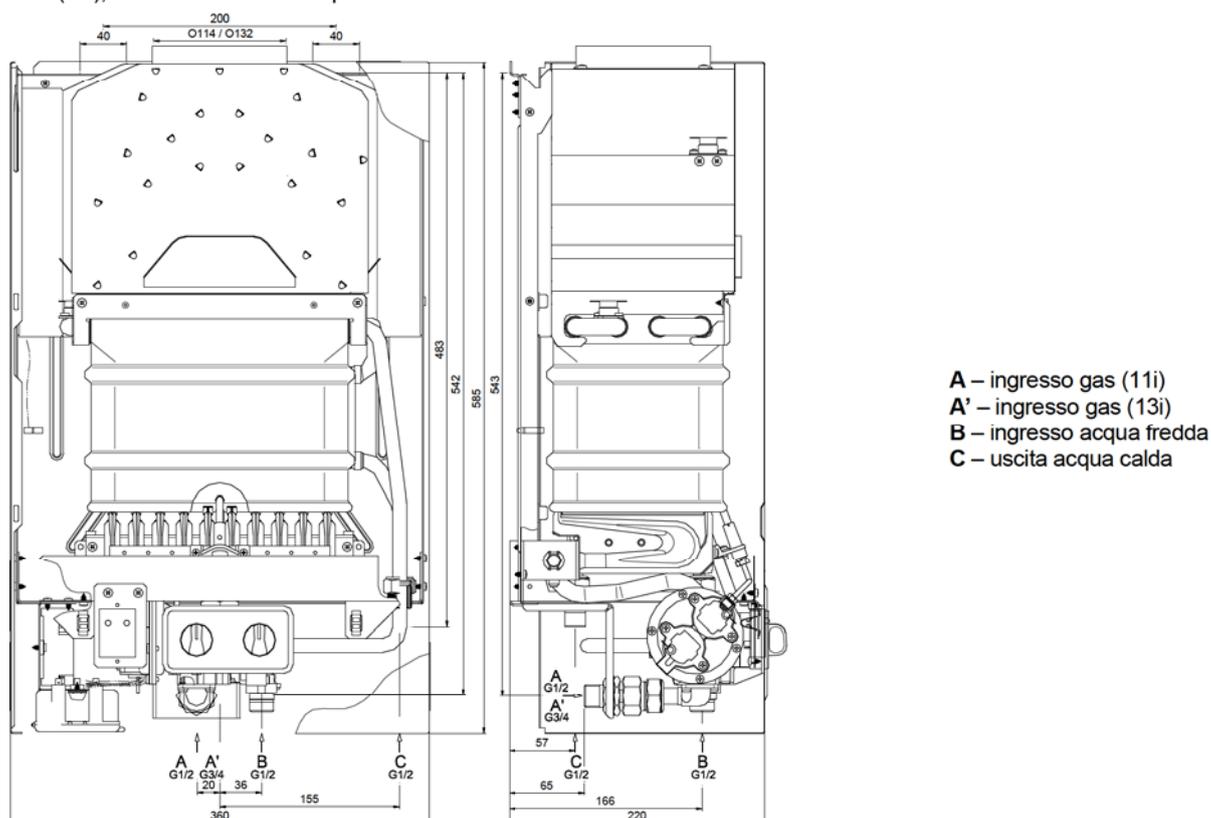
Le dimensioni principali di installazione (in mm)
